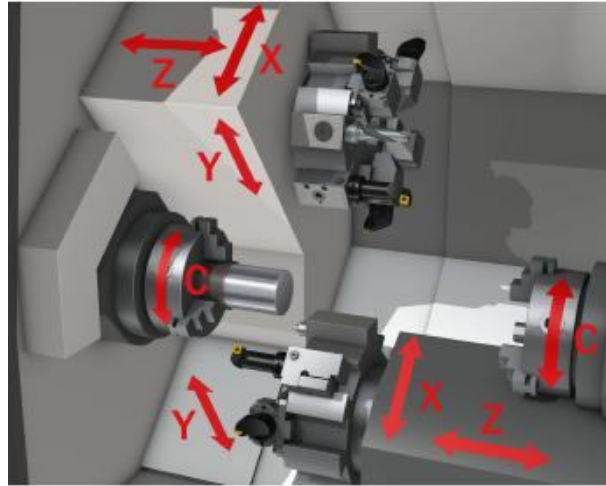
Схема перемещений рабочих узлов токарного обрабатывающего центра
